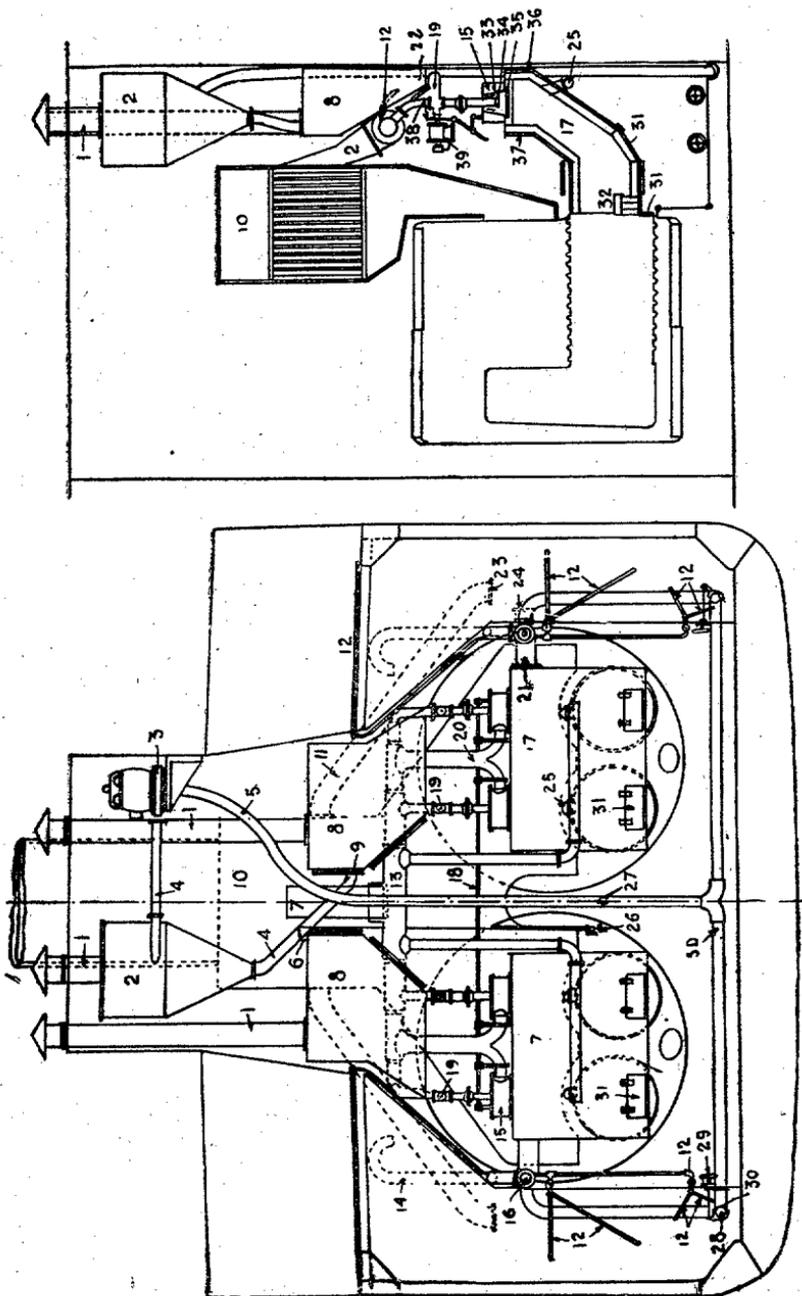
Sistema Brad aplicado a las calderas de un vapor para quemar carbón pulverizado.
